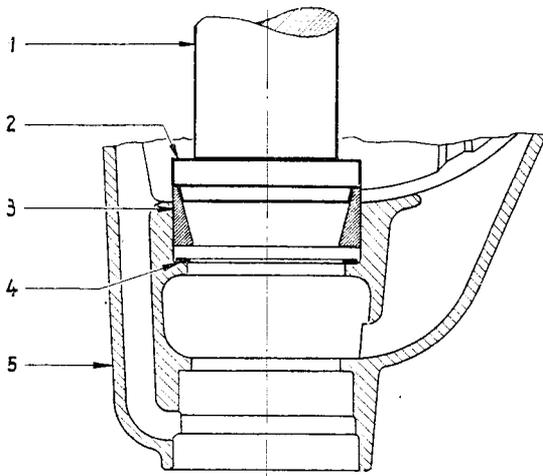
Äußeren Laufring des inneren Kegellagers in Hinterachsgehäuse einpressen
